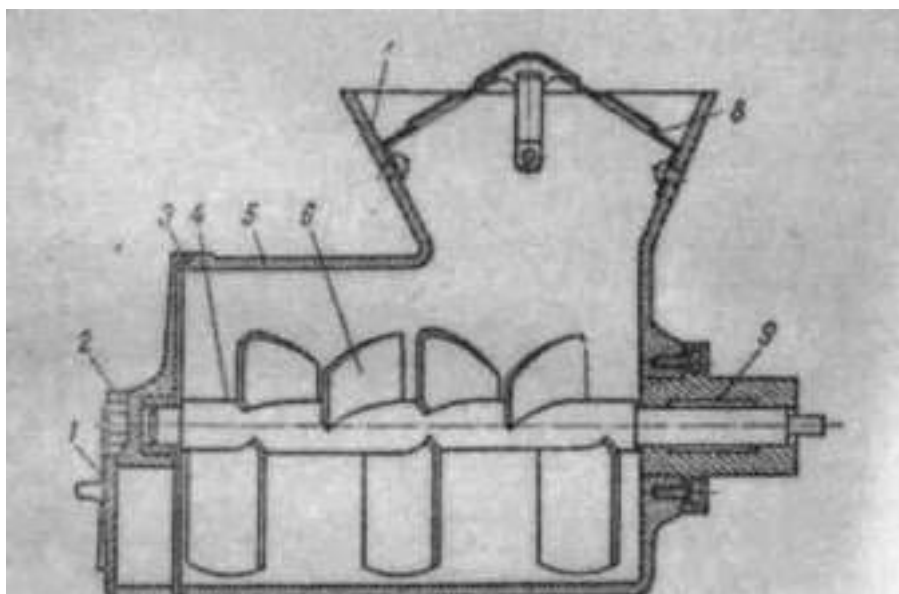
Фаршемешалка МС8-150: 1 - заслонка; 2 - откидной болт; 3 - крышка; 4 – рабочий вал; 5 - корпус; 6 -лопасть; 7 – загрузочный бункер; 8 - решетка; 9 - хвостовик.
